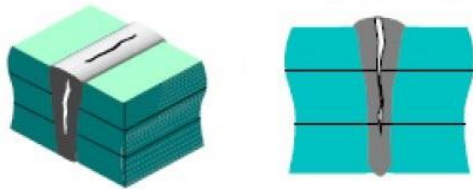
Schweißnahtfehler „Riss“ [6]
